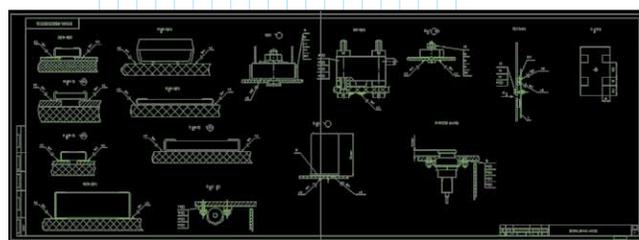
Продолжение размещения (вариант 1) на листе 2 сборочного чертежа печатной платы (слой TOP Assy – зеленый цвет)
